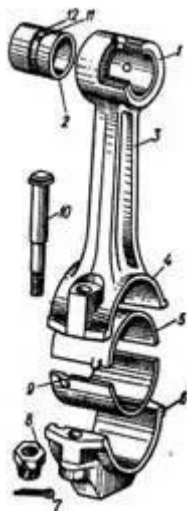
Шатун і шатунні підшипники: 1 – верхня головка; 2 - втулка верхньої головки; 3 - стержень; 4 - нижня головка; 5 - вкладиш шатунного підшипника; 6 - кришка нижньої головки; 7 – шплінт; 8 – гайка; 9 - вус-фіксатор; 10 - шатунний
